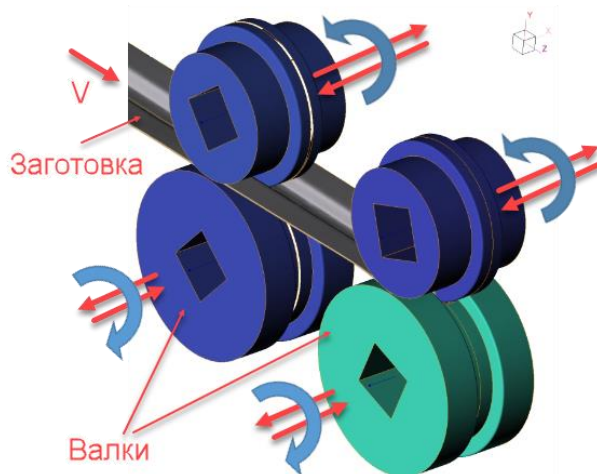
3D-моделі валків двох останніх клітей (стрілками позначені напрями обертання та руху заготовки)
